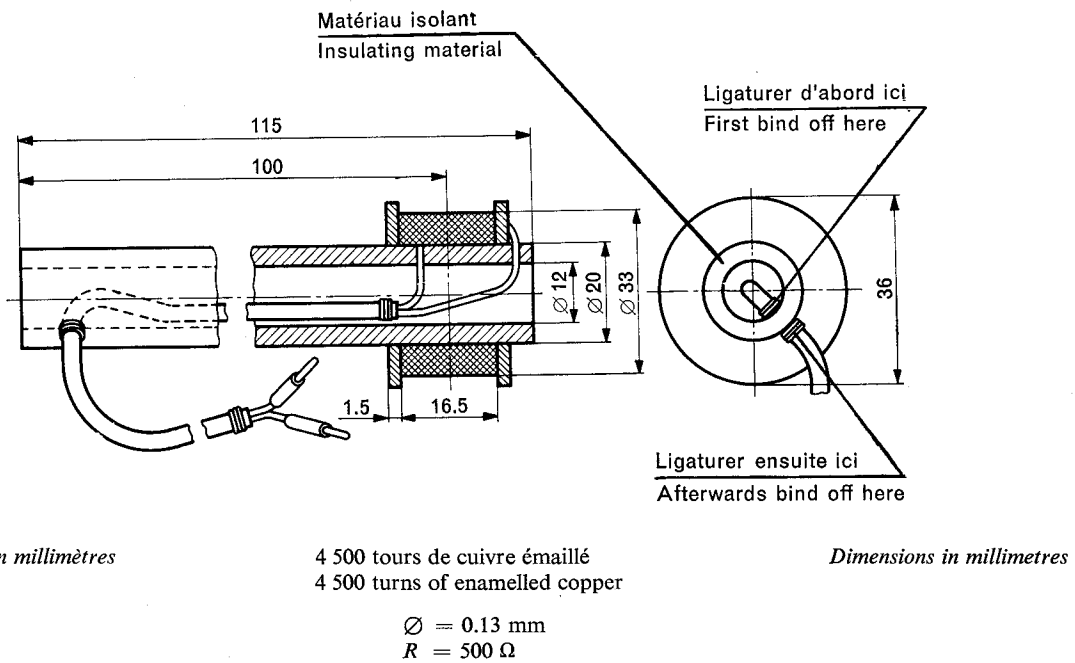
Bobine exploratrice pour la mesure de l'intensité des champs magnétiques.
